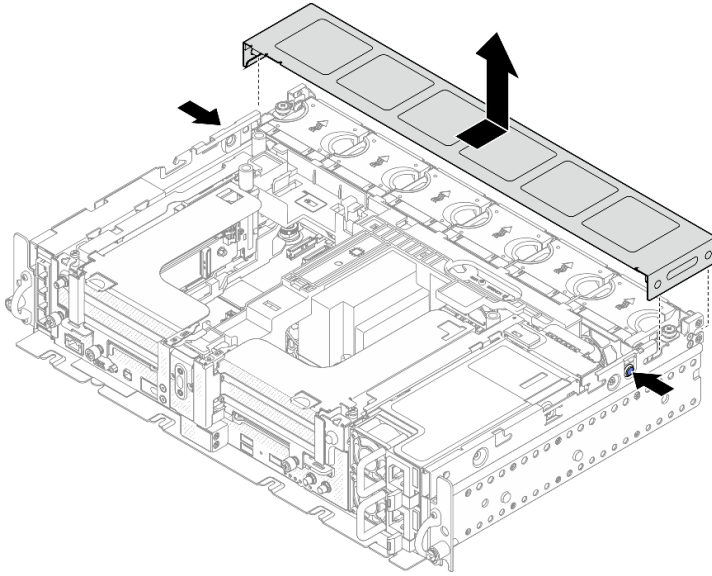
Extracción de la cubierta del ventilador (300 mm)
